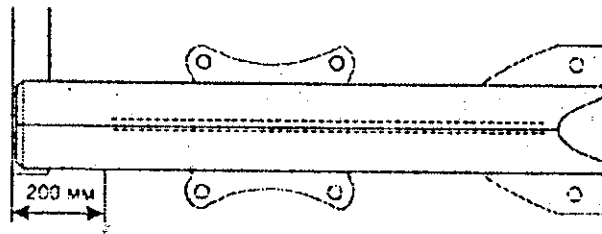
Контроль сварного шва верхней стенки продольной балки рамы
